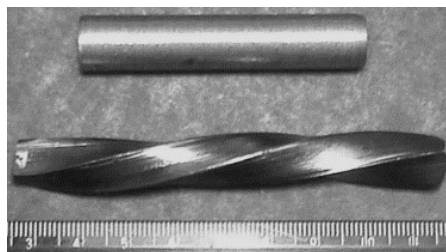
Заготовки из стали 09Г2С до (а) и после (б) комбинированной обработки
